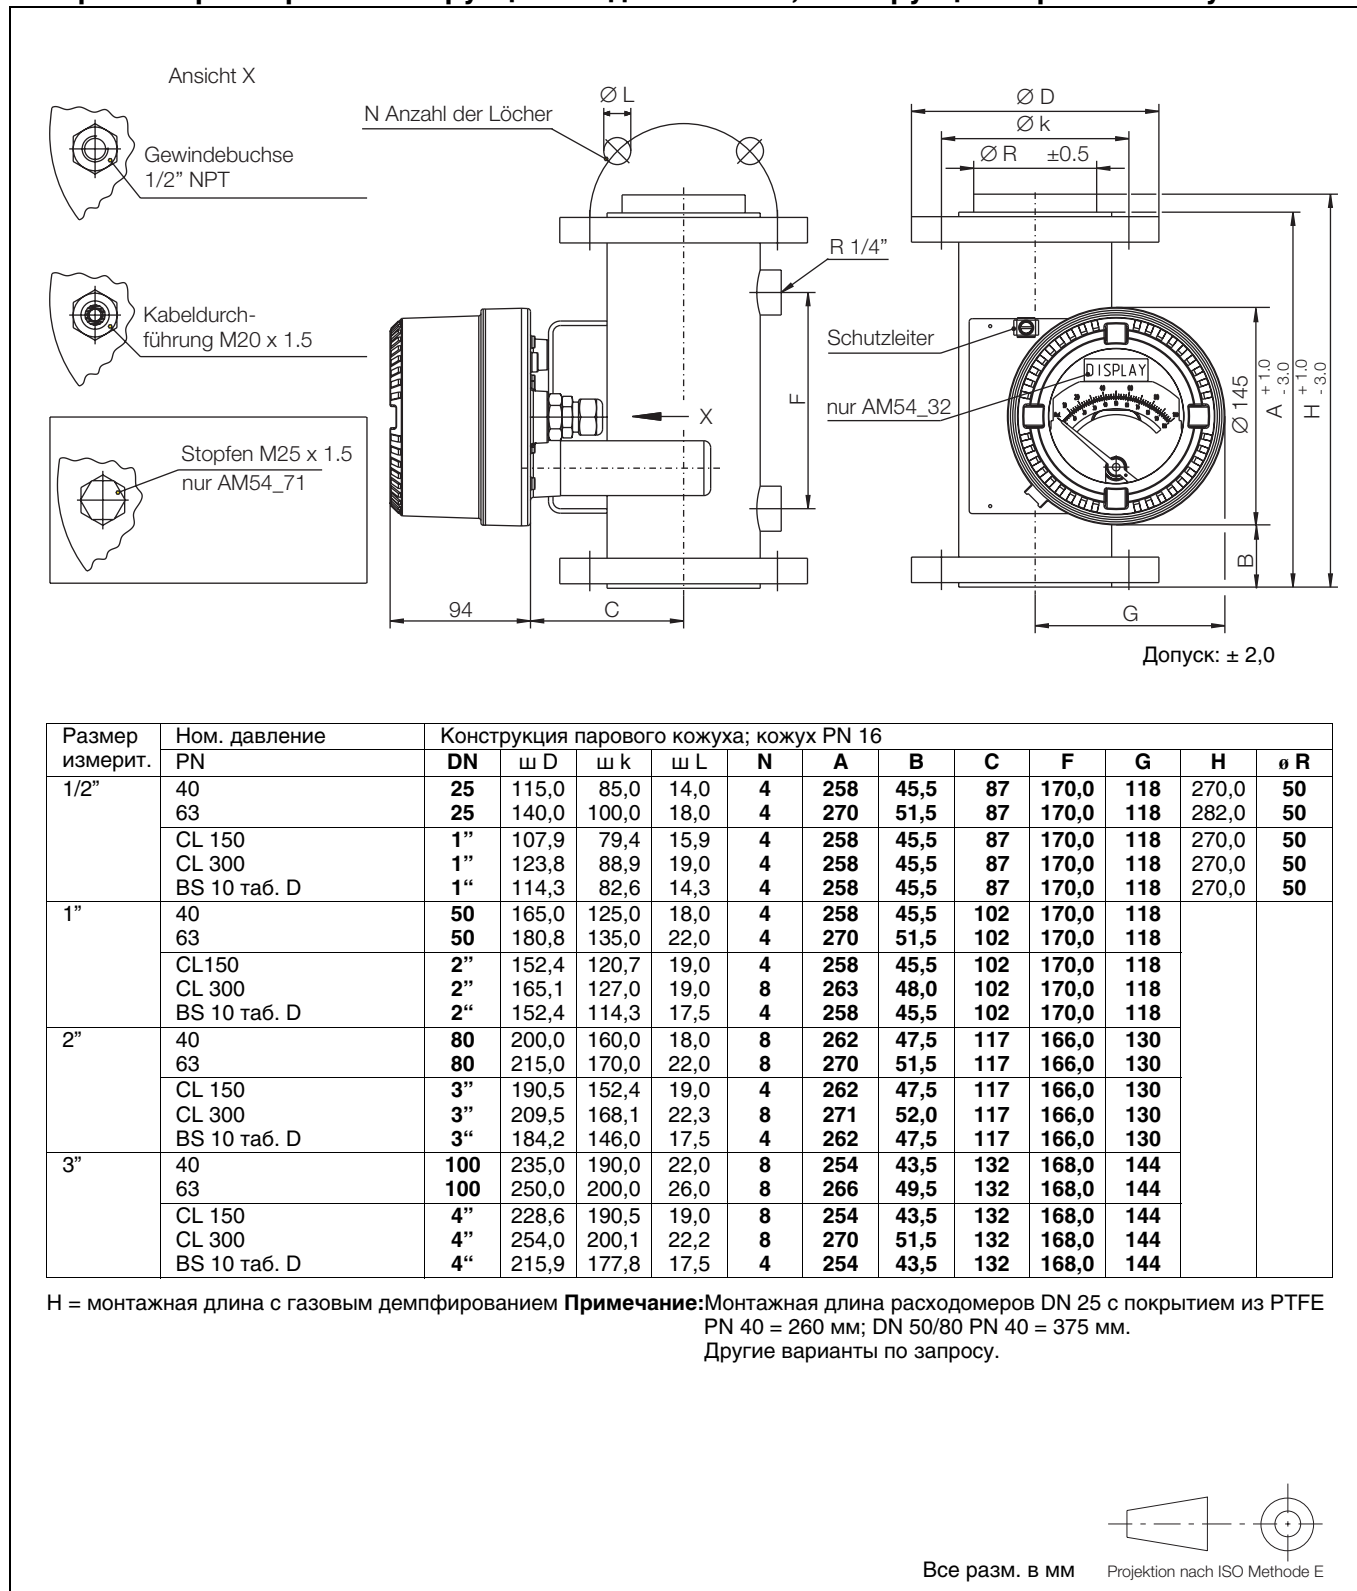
Габаритные размеры и соединители для конструкции 250 (конструкция с паровым кожухом).
